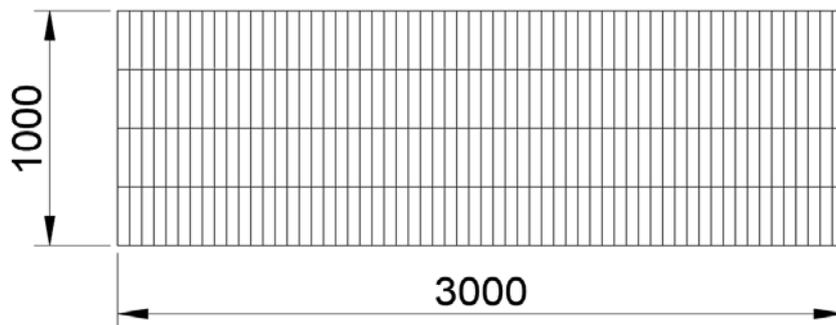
Distribución de la pieza en la chapa. Parte 5.
